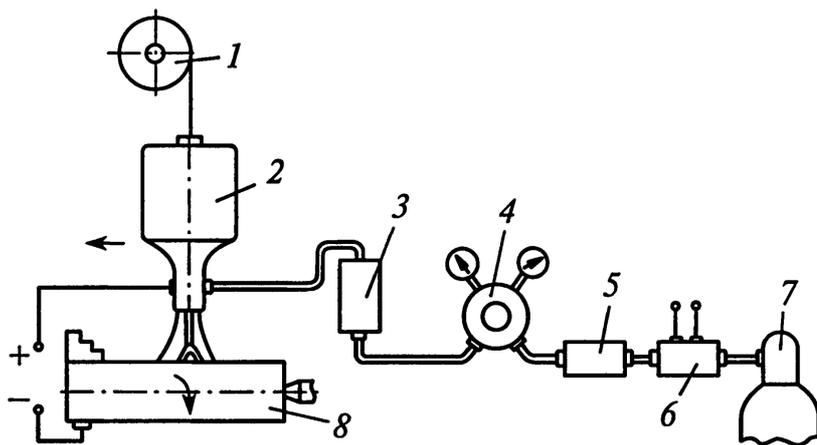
Схема установки для дуговой наплавки в углекислом газе: 1 – кассета с проволокой; 2 – наплавочный аппарат; 3 – расходомер; 4 – редуктор; 5 – осушитель; 6 – подогреватель; 7 – баллон с углекислым газом; 8 – деталь
